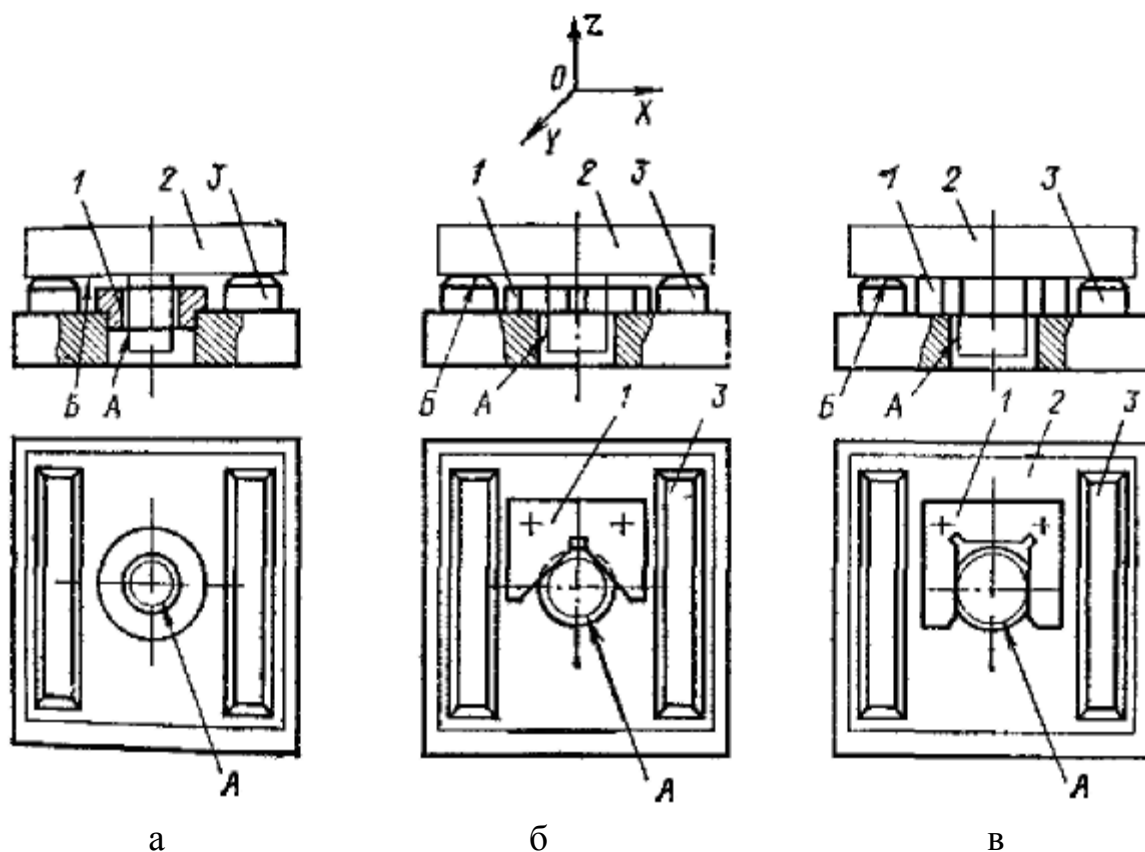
Способы базирования заготовки дополнительной базой в виде наружной цилиндрической поверхности, ось которой перпендикулярна базе, уже получившей базирование.
